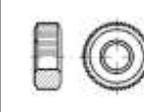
Конструкция заготовок гаек с боковым рифлением
